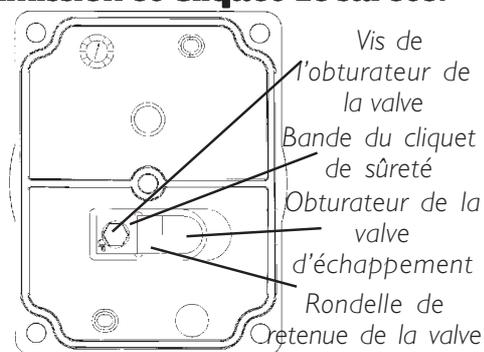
INSTALLATION D'UN OBTURATEUR NEUF DE VALVE D'ÉCHAPPEMENT, DE LA RONDELLE DE RETENUE DE LA VALVE ET DU CLIQUET DE SURETE
